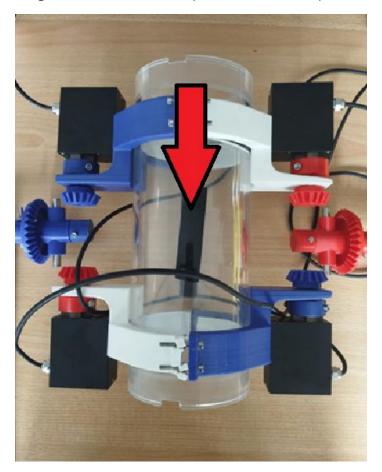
Positionnement de l'ensemble des pièces lors de l'assemblage final
